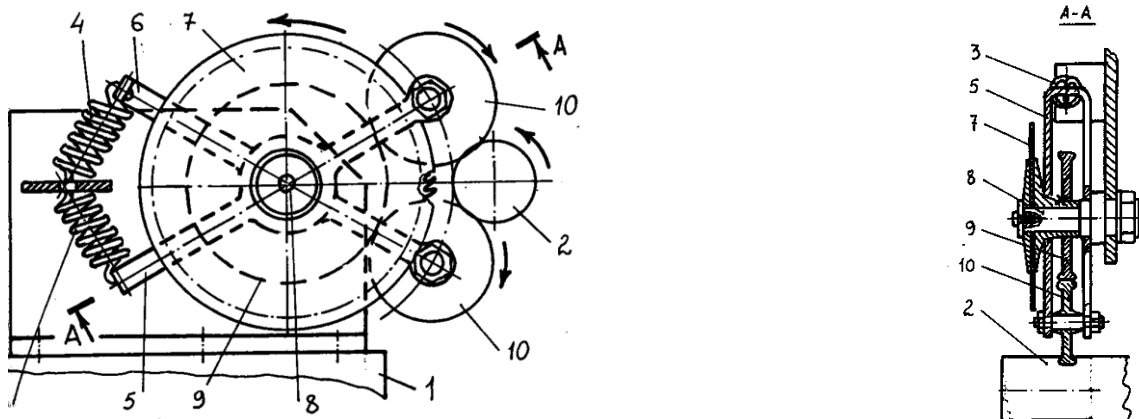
Пристрій для відрізки деталей по а.с. СРСР №1604526
